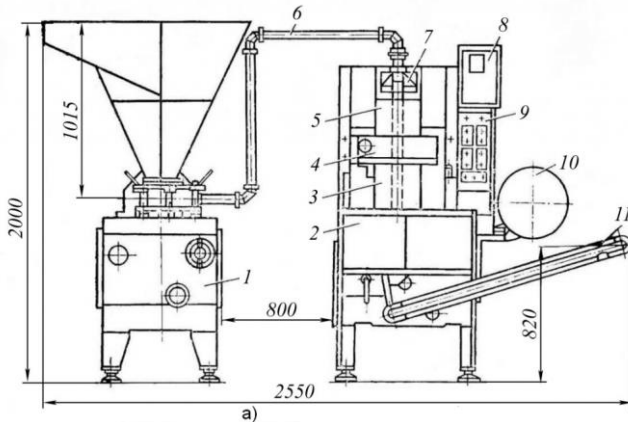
Агрегат М1-ФУР для формування варених ковбас(загальний вигляд): 1 - механізм нагнітання фаршу; 2 - механізм формування батонів; 3 - механізм утворення оболонки; 4 - протяжний механізм; 5 - зварювальний механізм; 6 - фаршепровід; 7 - рукавотворювач; 8 - механізм утворення скріпок; 9 - механізм накладання скріпок; 10 - рулон плівки; 11 - транспортер
